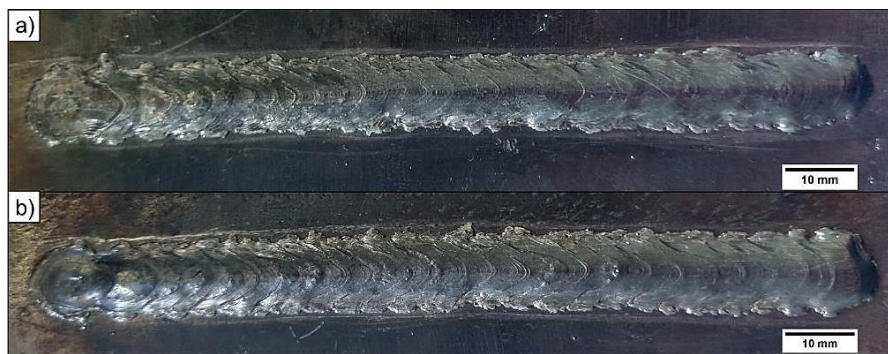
Cordões de solda: a) Sem a técnica de switchback; b) com a técnica de switchback com avanço 4 e reversão 2
